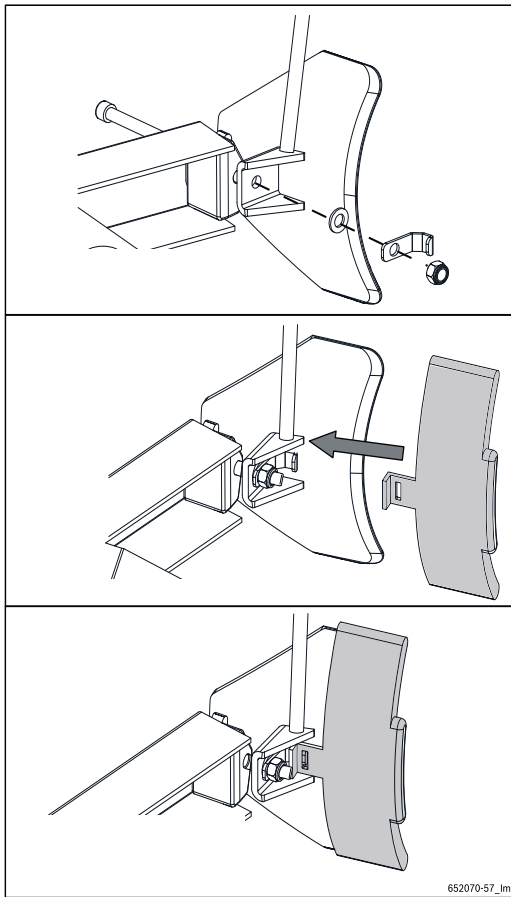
Montaje de elemento protector para la paleta de destalonado
